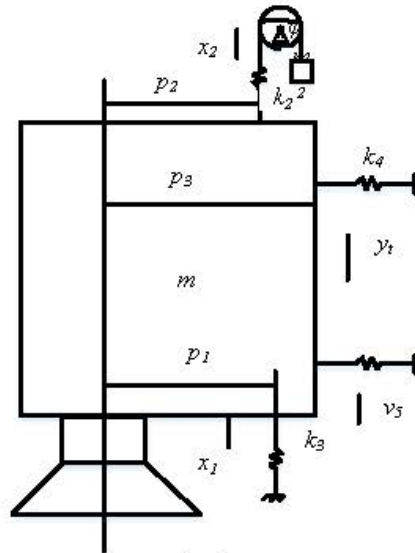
Розрахункова схема бабки вертикального фрезерного верстата
